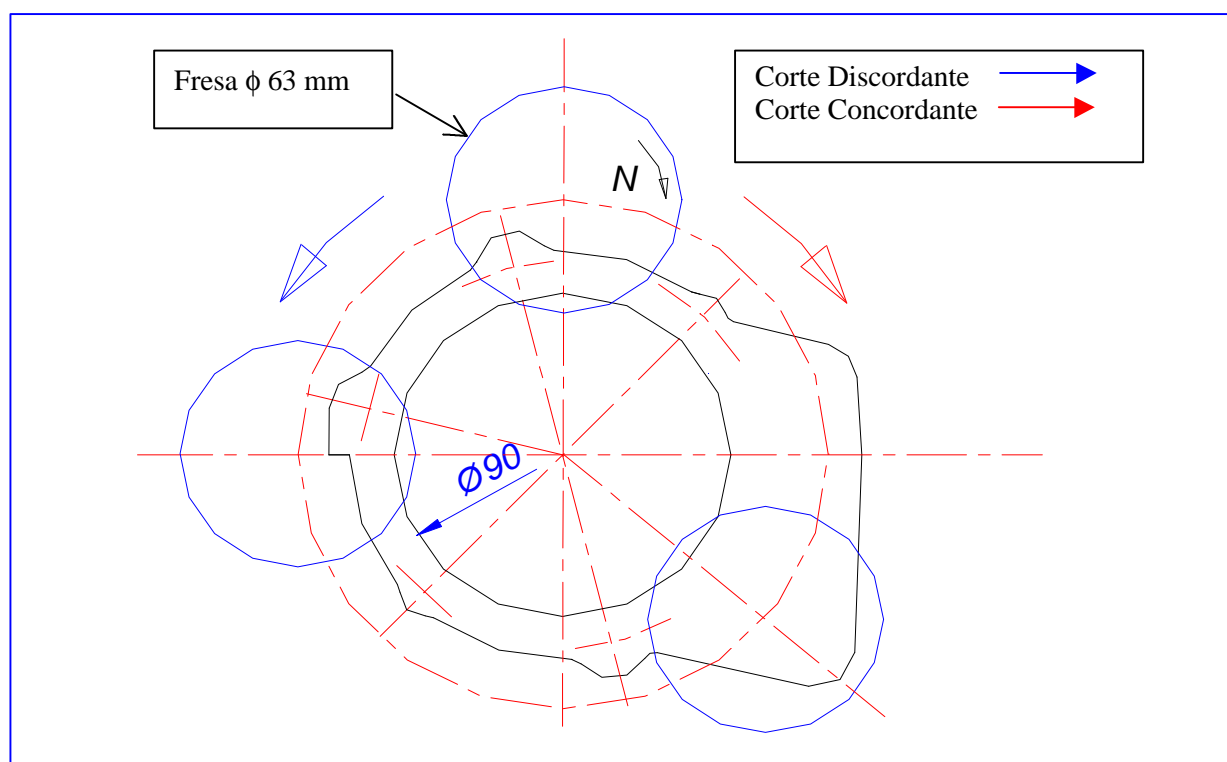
Usinagem da Superfície 3 nos sentidos concordante e discordante
